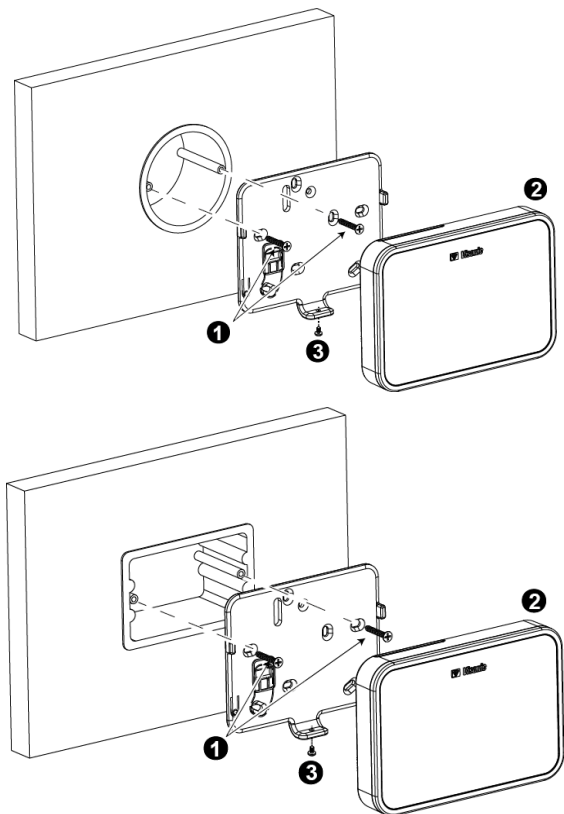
Montagem em Parede com o Conector Elétrico Externo
